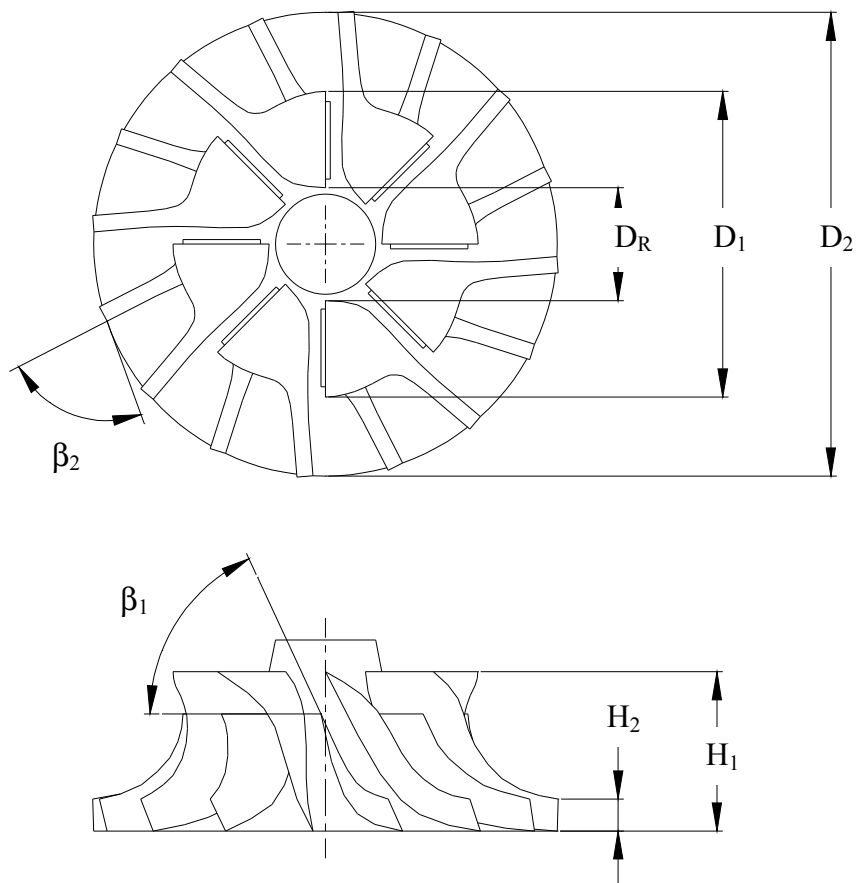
Dimensões Características do Rotor do Compressor
